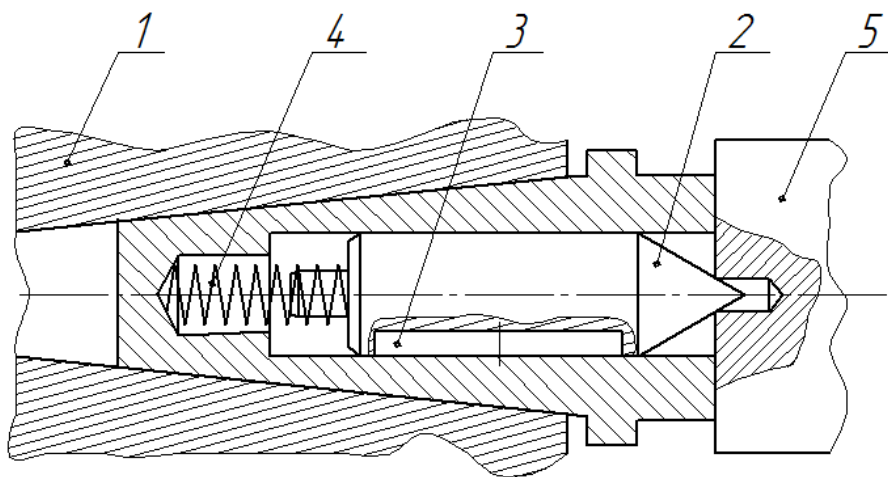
Будова плаваючого центра для верстатів із ЧПК: 1 – корпус; 2 – центр; 3 – шпонка; 4 – пружина, 5 – деталь
